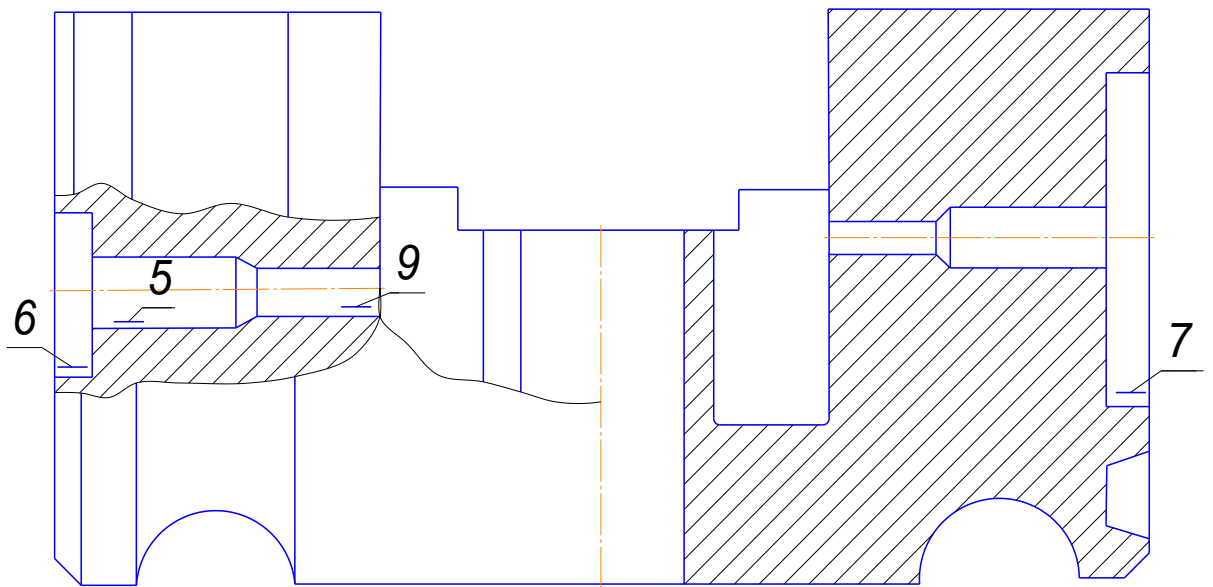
Ескіз обойми з нумерацією поверхонь
